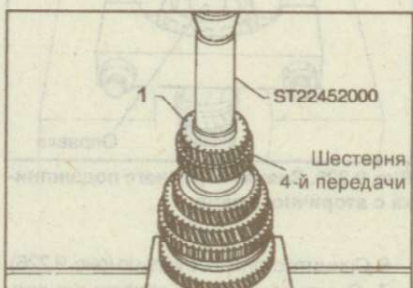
Установка шестерни 5-й передачи (1) на вторичный вал
